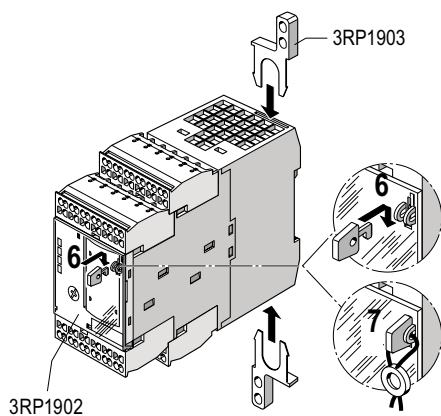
3TK2826 mit plombierbarer Abdeckklappe. Befestigung des Geräts mit Hilfe von Einstecklaschen für Schraubbefestigung.
